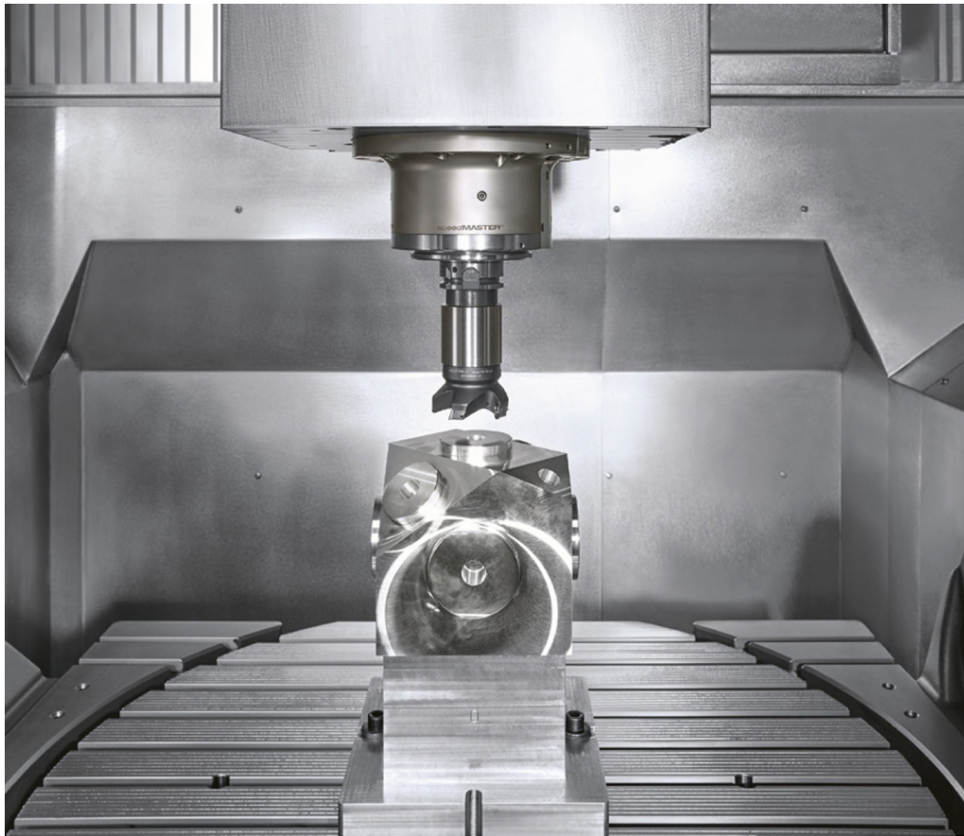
Für die Bearbeitung von Metall werden eine sehr steife Maschine und starke Motoren benötigt. Die Abbildung zeigt die Innenansicht einer DMU 95 monoblock von DMG Mori (© DMG Mori).
